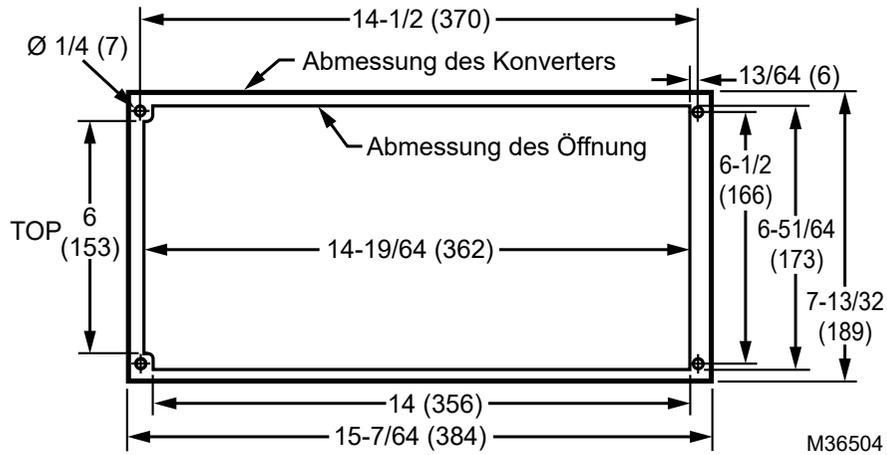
Abmessungen Ausschnitt für Flanschmontage für MI4 [Unit: Inches (mm)]
